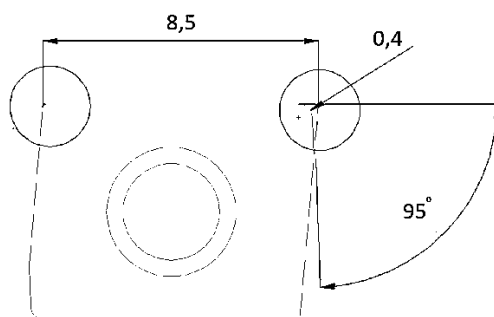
Сменная пластина фрез Coro Mill 490R-08T304M-PL 1030
